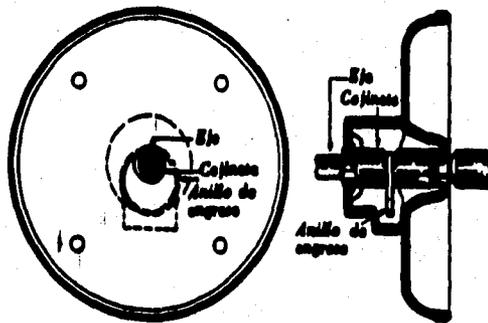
Cojinete de resbalamiento montado en un escudo.
